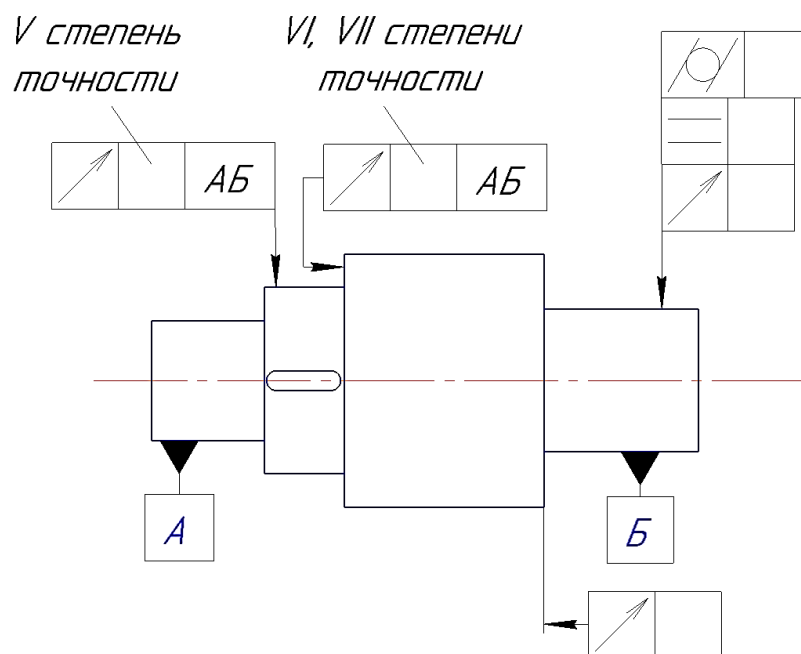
Требования к присоединительным размерам валов для установки зубчатых колес
